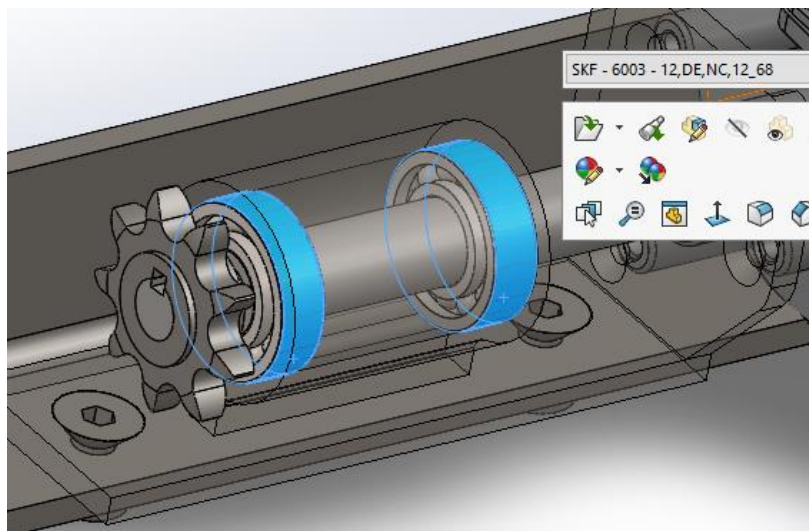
Ensamblaje de rodamientos SKF 6003 en el mecanismo. El autor.
